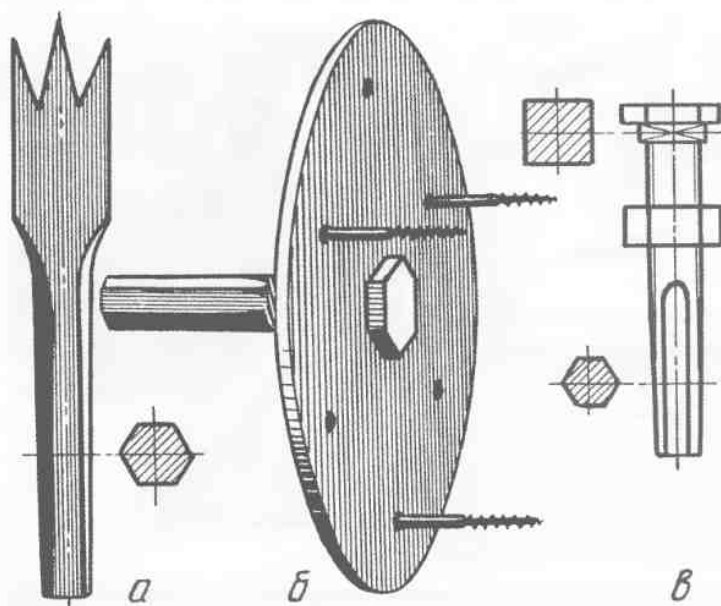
Державки, передающие при точении вращательное движение от патрона электродрели деревянной заготовке: а — трезубец (изготавливается ковкой) для небольших деталей; б — планшайба для крупных деталей; в — чертеж оси планшайбы
